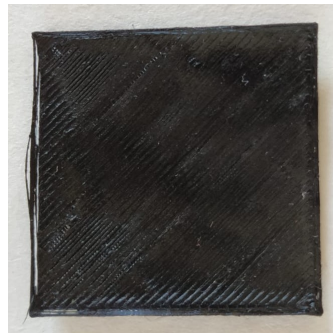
Placa impresa boq.0,4mm, ec=0,15mm
